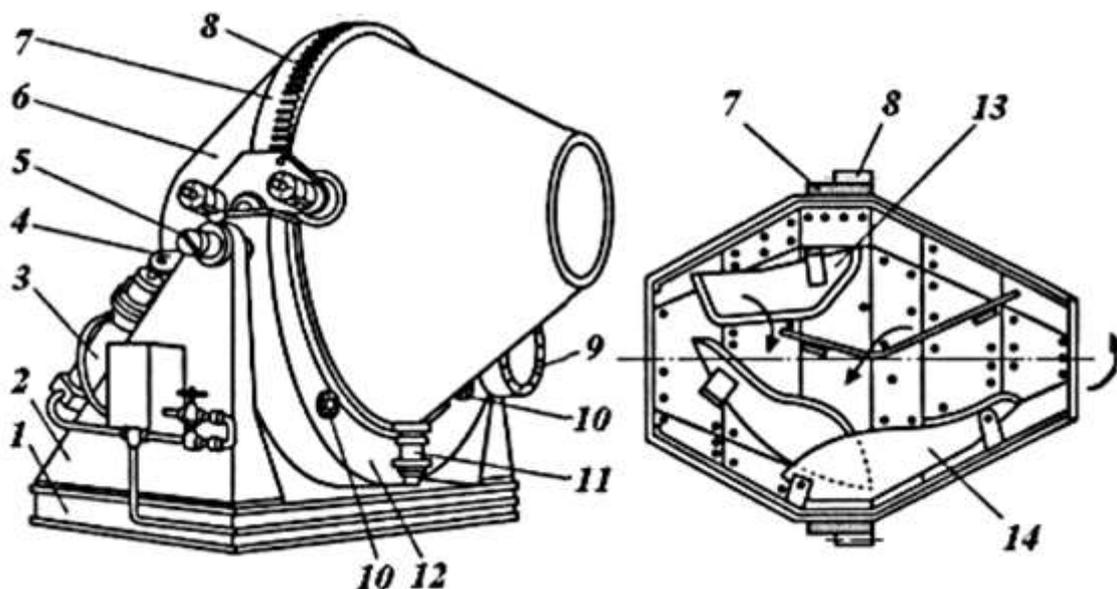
Гравитационный смесительный барабан: 1-станина; 2-стойка; 3-пневмоцилиндр наклона траверсы с барабаном; 4-кронштейн; 5-шип траверсы; 6-барабан; 7-обод; 8-зубчатый венец; 9-двигатель; 10-опорные ролики (сзади траверсы); 11-упорный ролик, удерживающий барабан при наклоне (три пары); 12 - траверса; 13, 14-перемешивающие лопасти.
